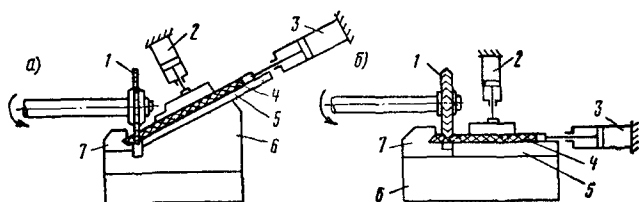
Способы резки заготовок текстолитовых клиньев:
